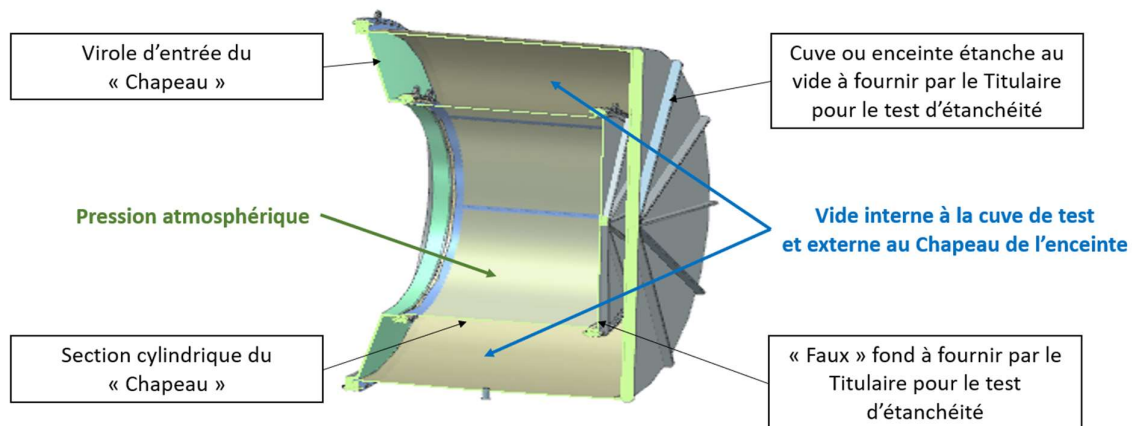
Virole d'entrée et section cylindrique du « Chapeau » assemblé pour le test d'étanchéité
